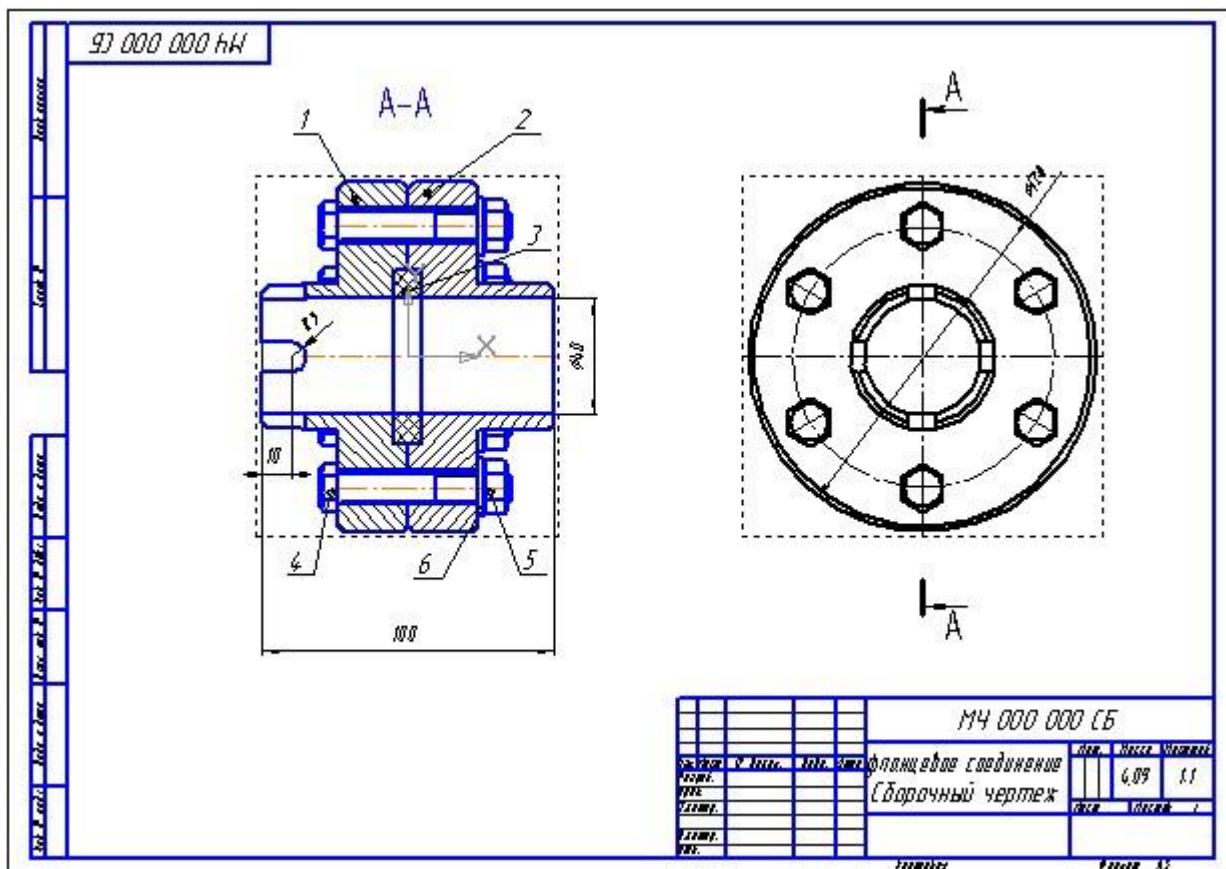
Складальний кресленик фланцевого з'єднання
